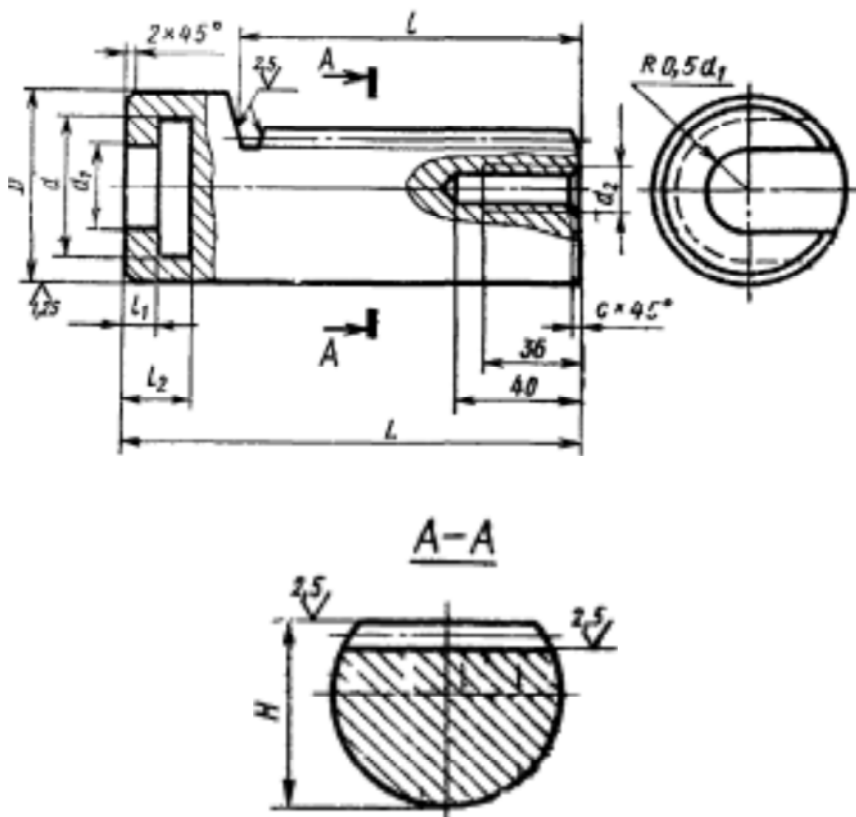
Конструкция зубчатой рейки приспособления для удаления стержней
